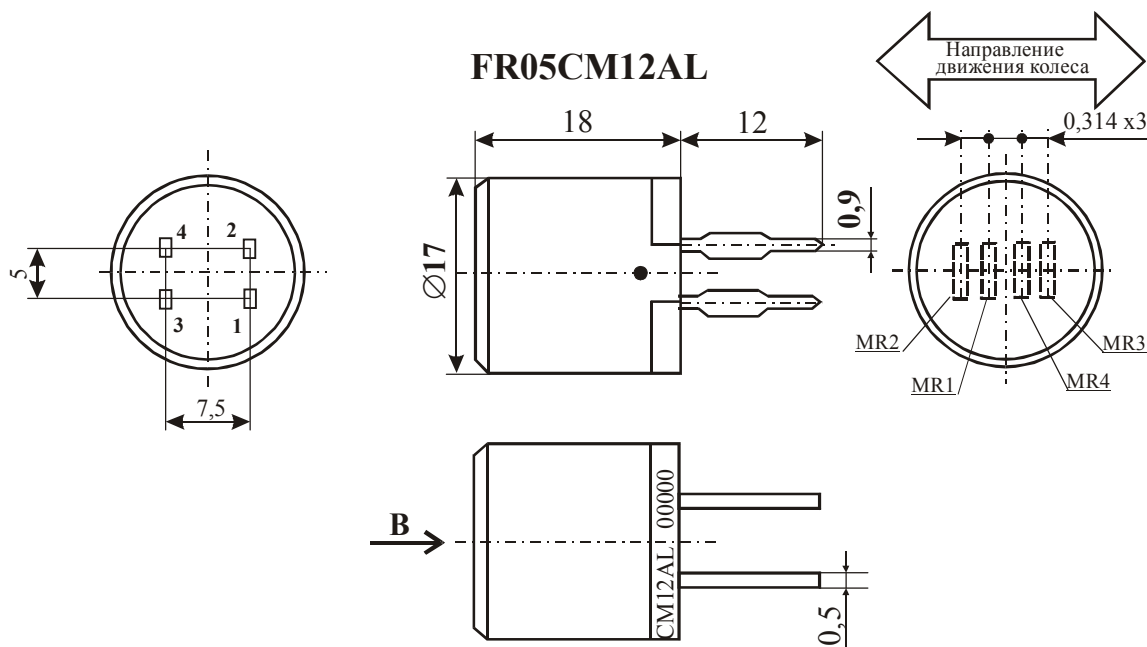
Внешний вид и габаритные размеры датчиков типа FR05CM12AL
